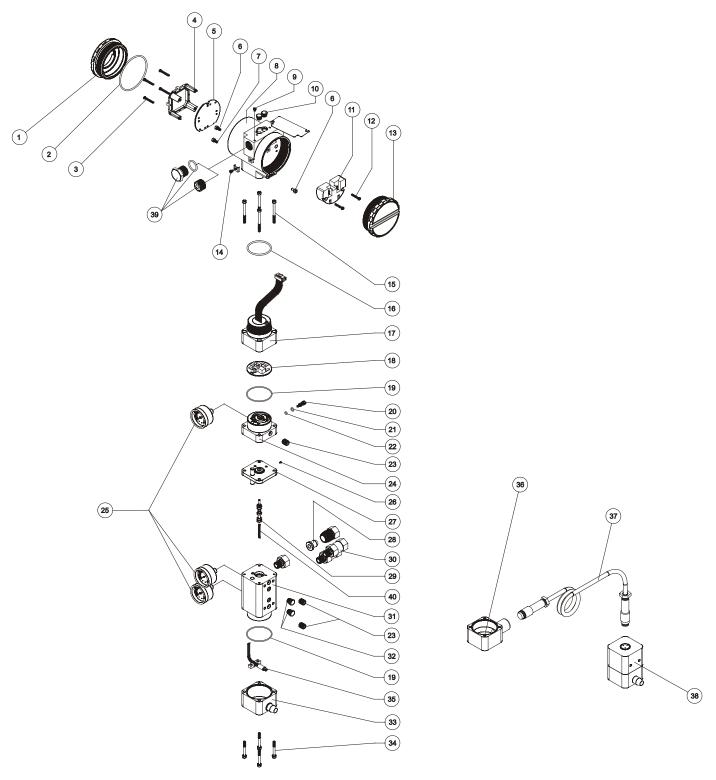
Vista Explodida do Posicionador FY301 do ACP
